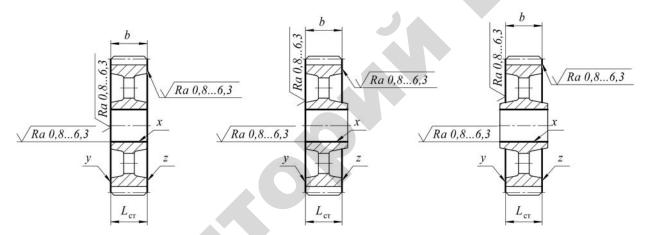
Шероховатости поверхностей, используемых в качестве установочных баз
